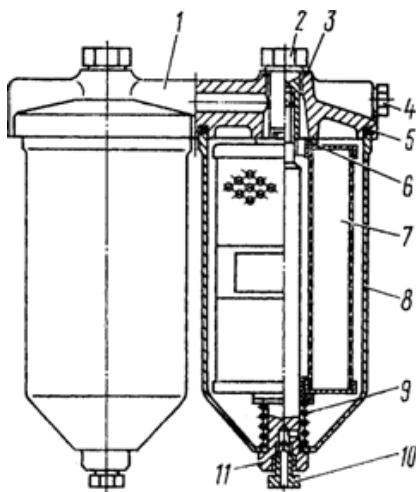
Фильтр тонкой очистки топлива: 1 – корпус; 2 – болт; 3 – шайба уплотнительная; 4 – пробка; 5, 6 – прокладки уплотнительные; 7 – элемент фильтрующий; 8 – колпак; 9 – пружина фильтрующего элемента; 10 – пробка сливная; 11 – стержень
